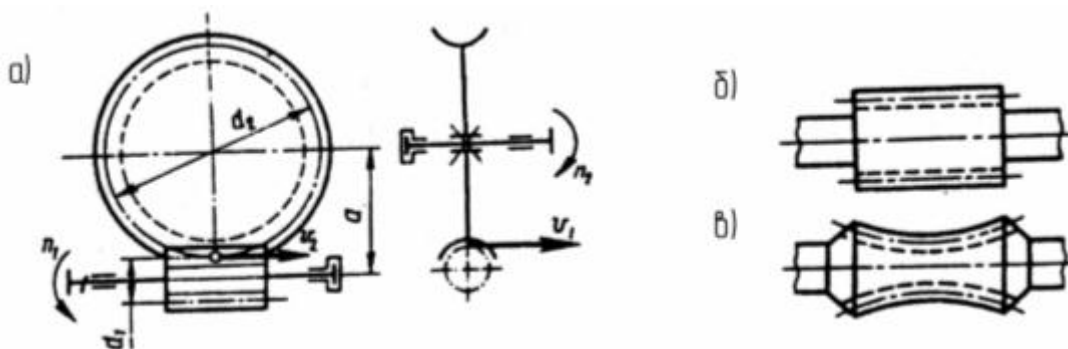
Схема черв'ячної передачі ліфтового редуктора.
